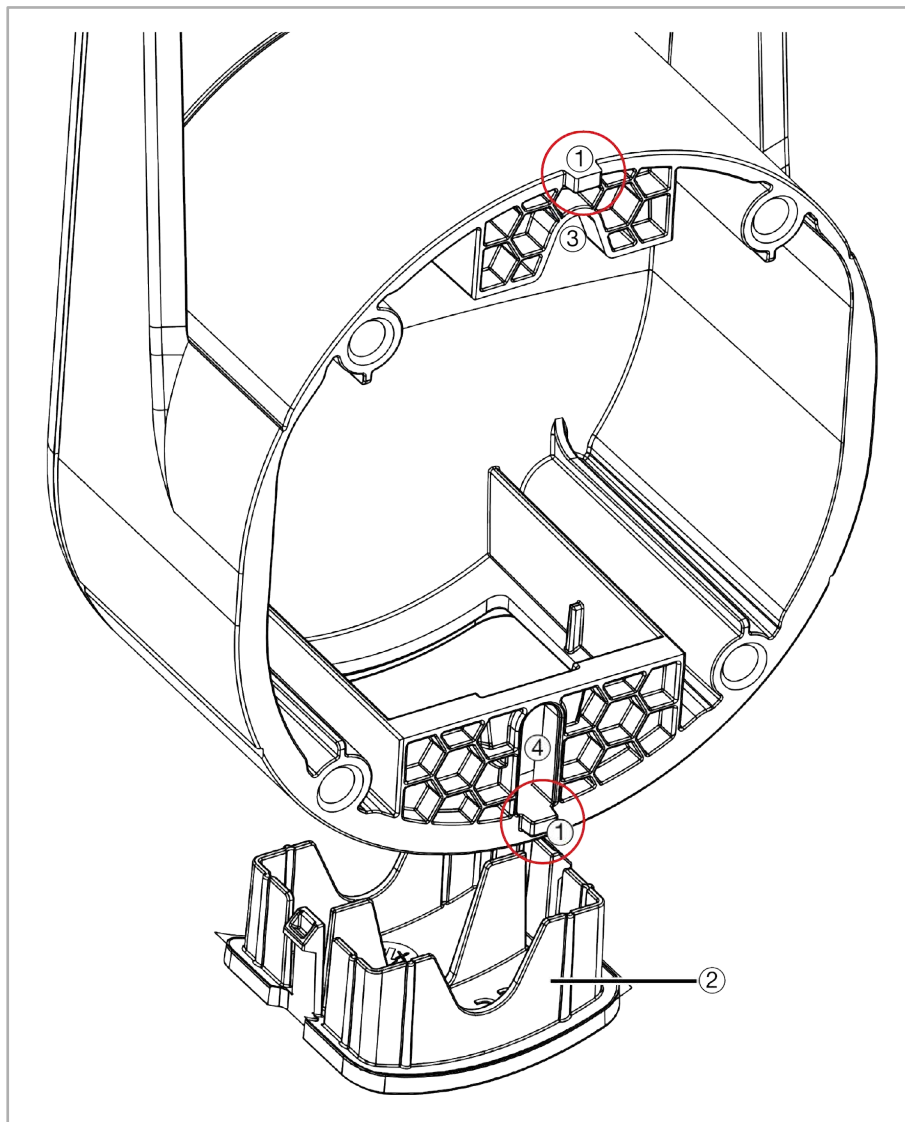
Montage des Kabelhalters an der Wand (Ansicht von der Rückseite)
